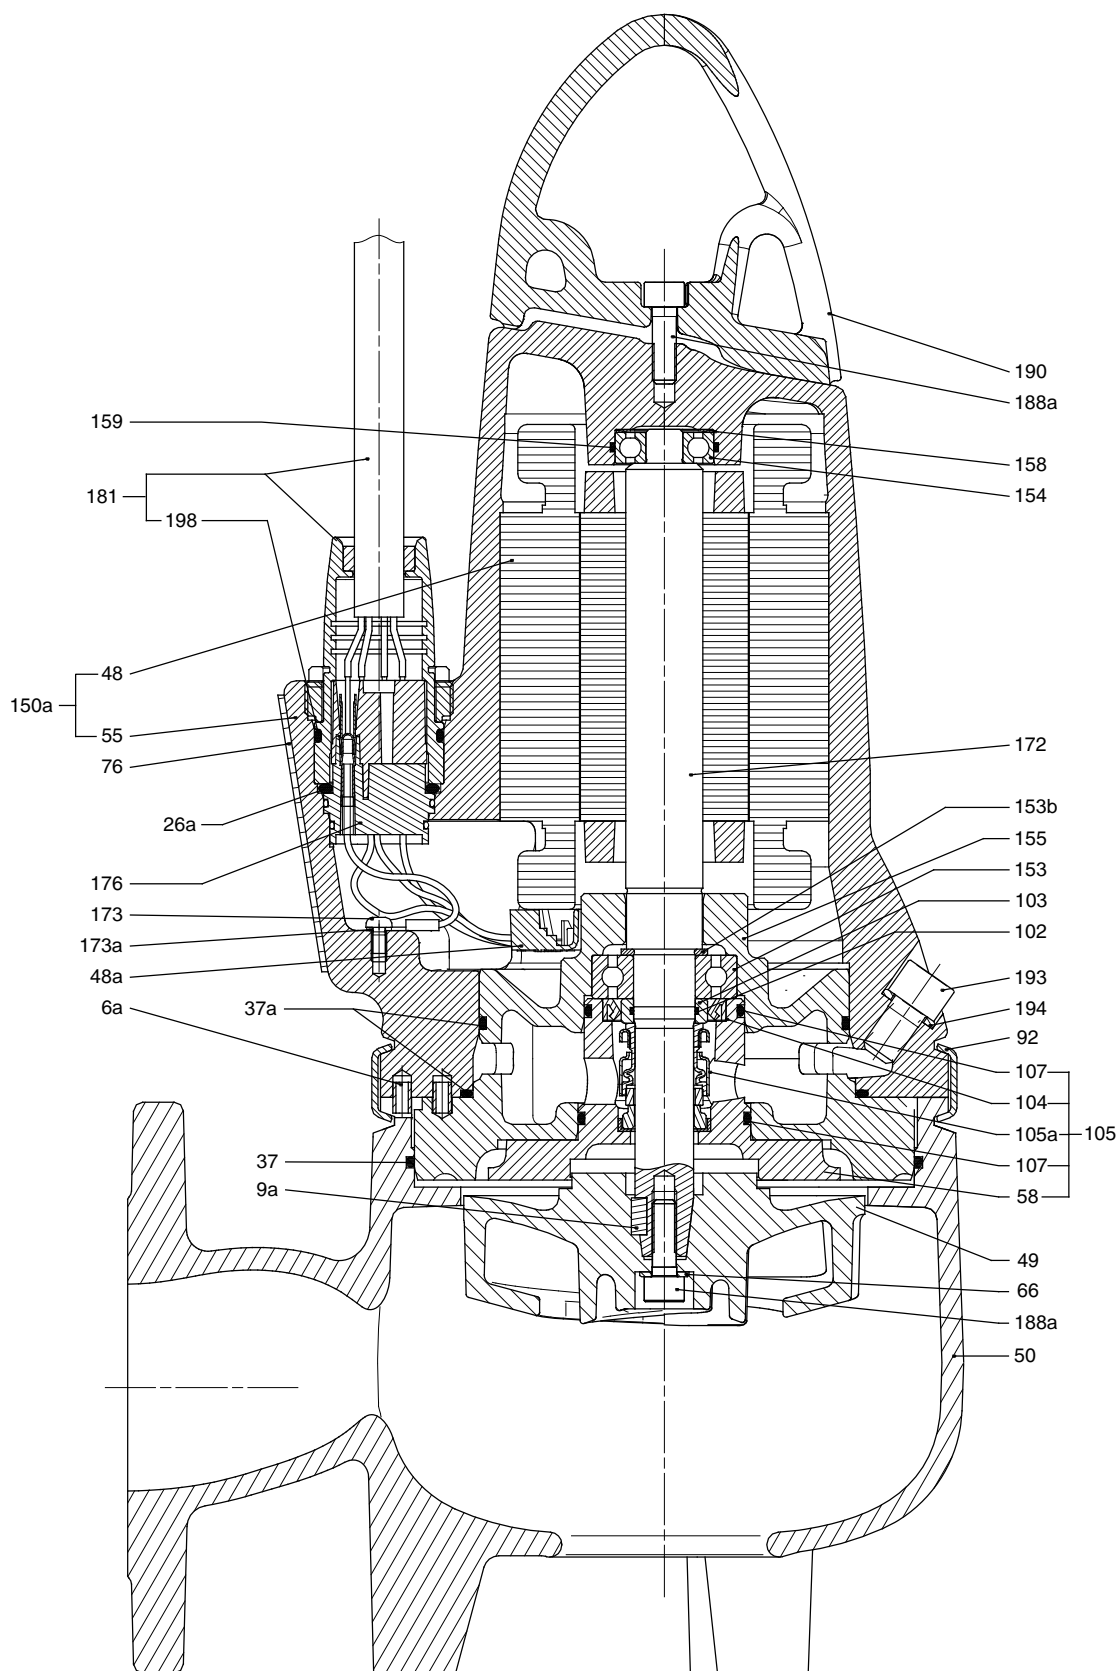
Rysunek przekrojowy SL1.50.65.09/11/15
